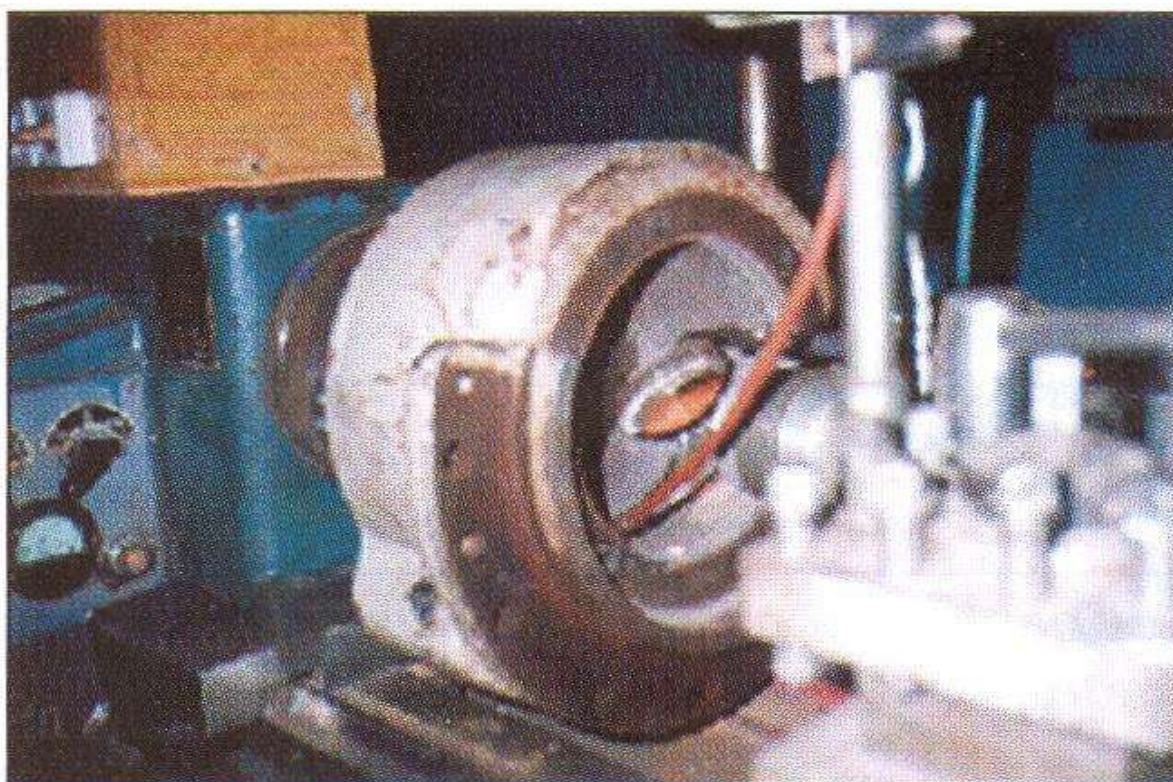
Корпус насоса при лазерной наплавке посадочных мест под подшипники
